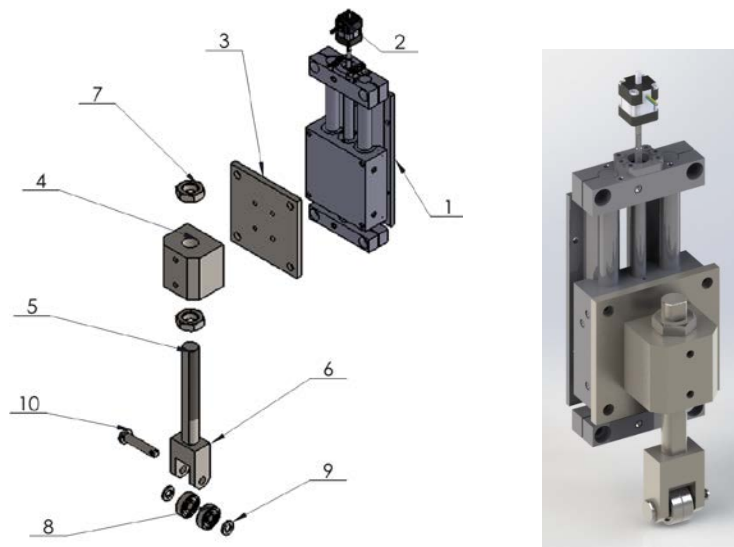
Mecanismo calçador, representado em vista isométrica explodida e montada
